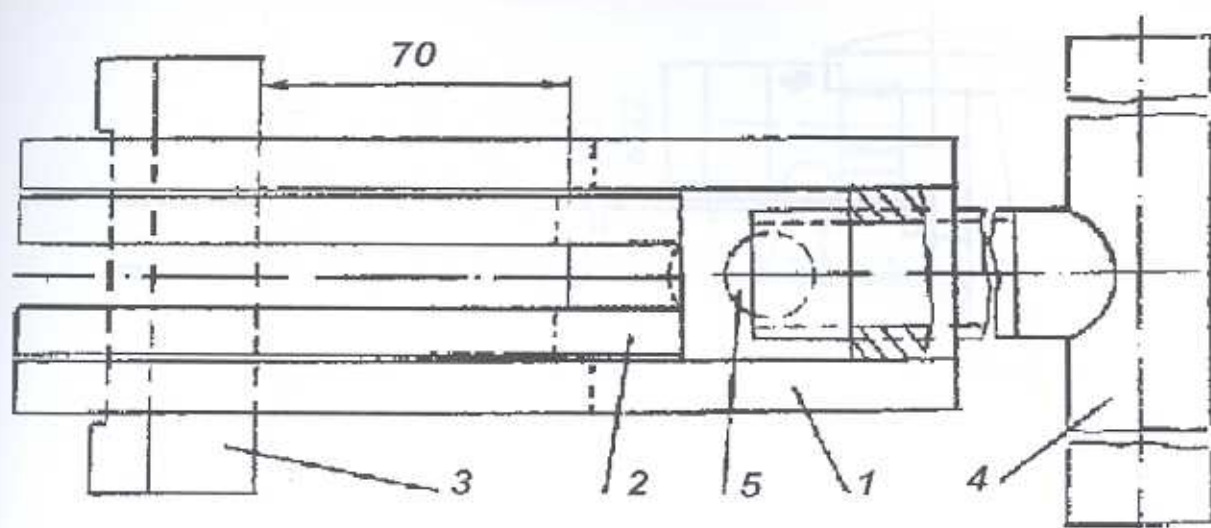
Приспособление для обрезки концов стержней статора:
